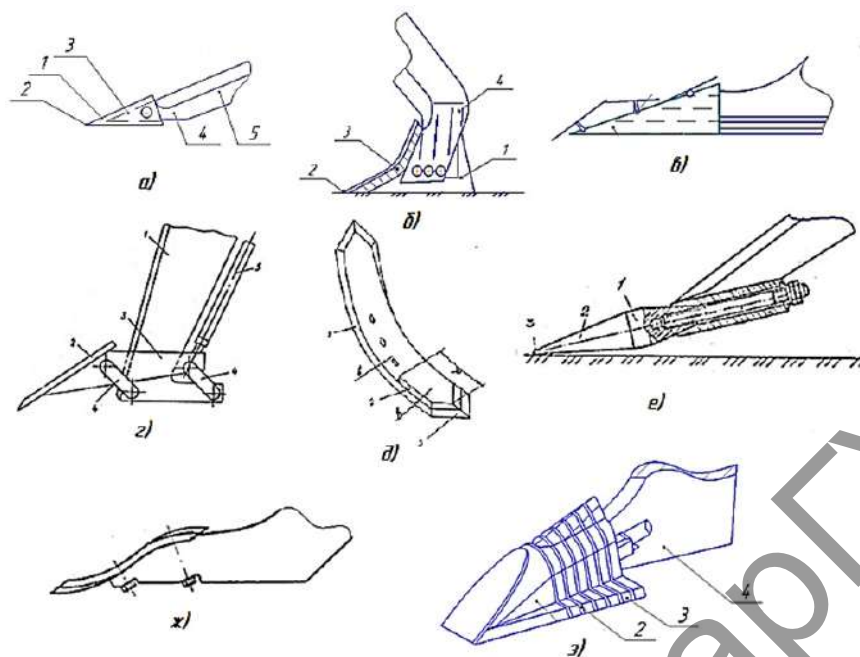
Патентный поиск рабочих органов глубокорыхлителей: а — Рабочий орган глубокорыхлителя Пат: 2263429 РФ; б — Упрочненное цилиндрическое долото Пат: 2269237 РФ; в — Гидроударное долото Пат:2415525 РФ; г — Шарнирное долото Пат: 1641209 РФ; д — Упрочненное долото Глубокорыхлителя Пат:2532971 РФ; е — ДренерПат:1790826 РФ; ж — Рабочий орган с S-образным долотом Пат: 1303051 РФ; з — Многослойное долото Пат: 1466668 РФ
